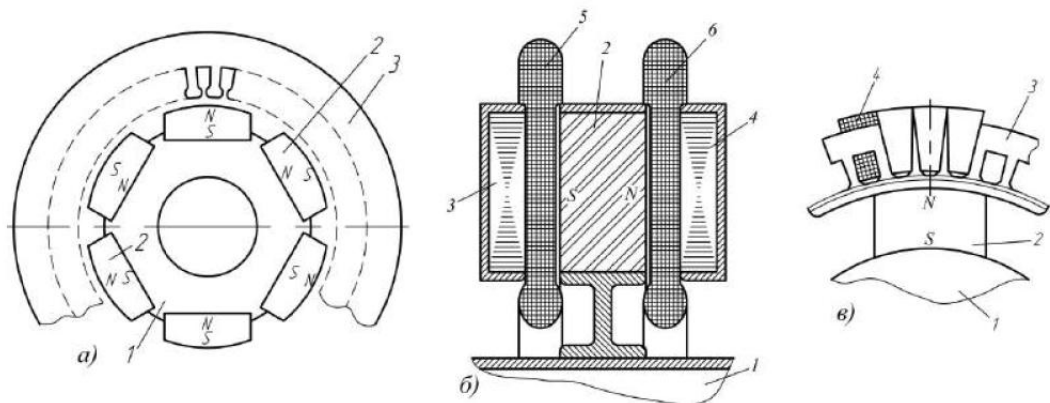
Багатополюсні моментні двигуни з постійними магнітами: а – шестиполіусний; б - багатополюсний торцевий; в – багатополюсний з кільцевою обмоткою управління.
